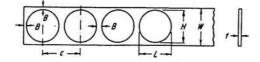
Disposición sencilla de una tira de material para cortar en troquel.
